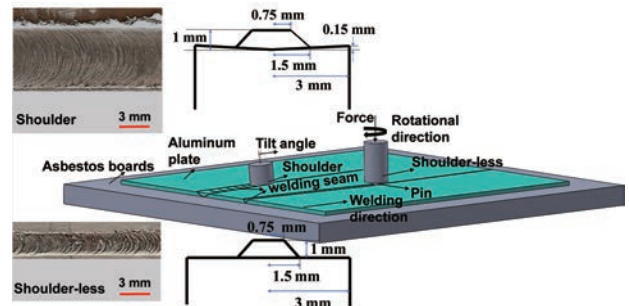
焊接过程示意、搅拌工具尺寸及焊缝表面成型
